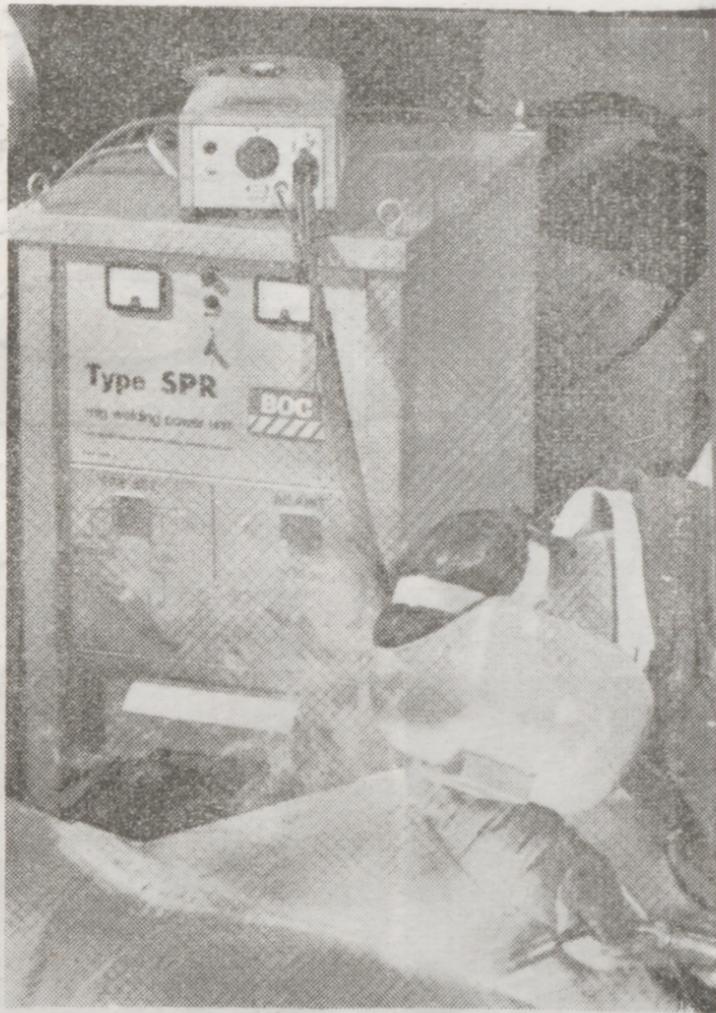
Equipo para la soldadura por arco pulsado.
